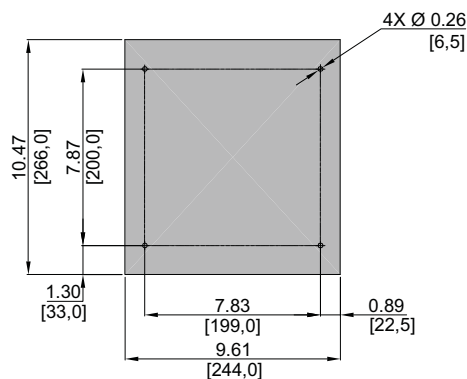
Dimensions des trous de montage et des découpes du couvercle du boîtier
